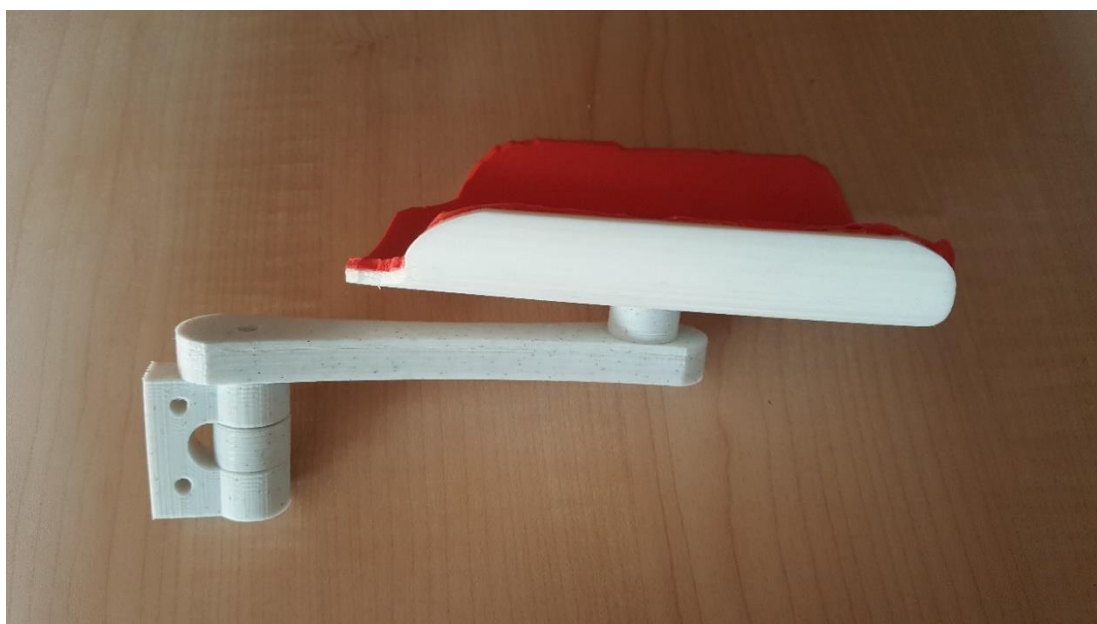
Conjunto de rótula y brazo de apoyo montado.
